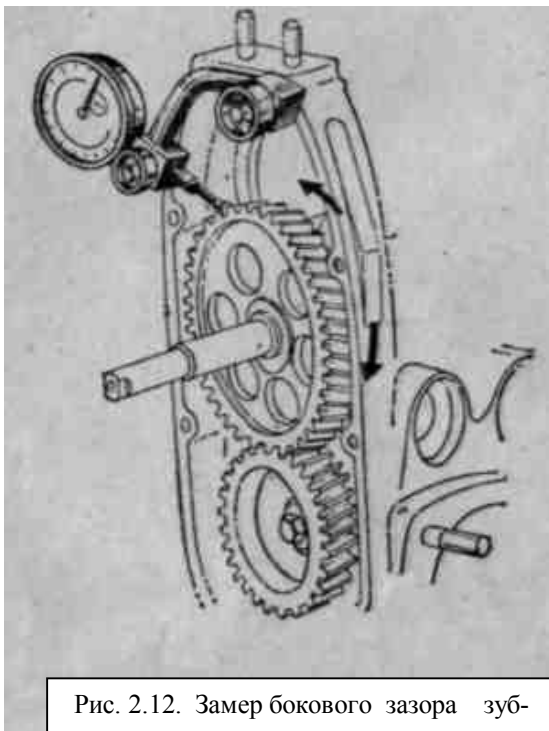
Замер бокового зазора зубчатых колес привода распределительного вала.
